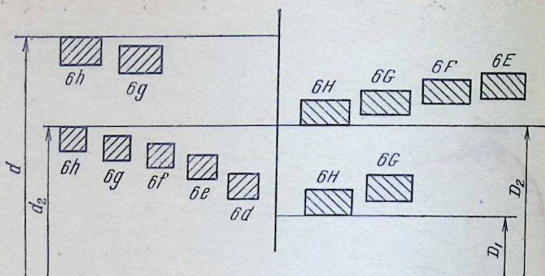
Расположение полей допусков резьб с зазором.
